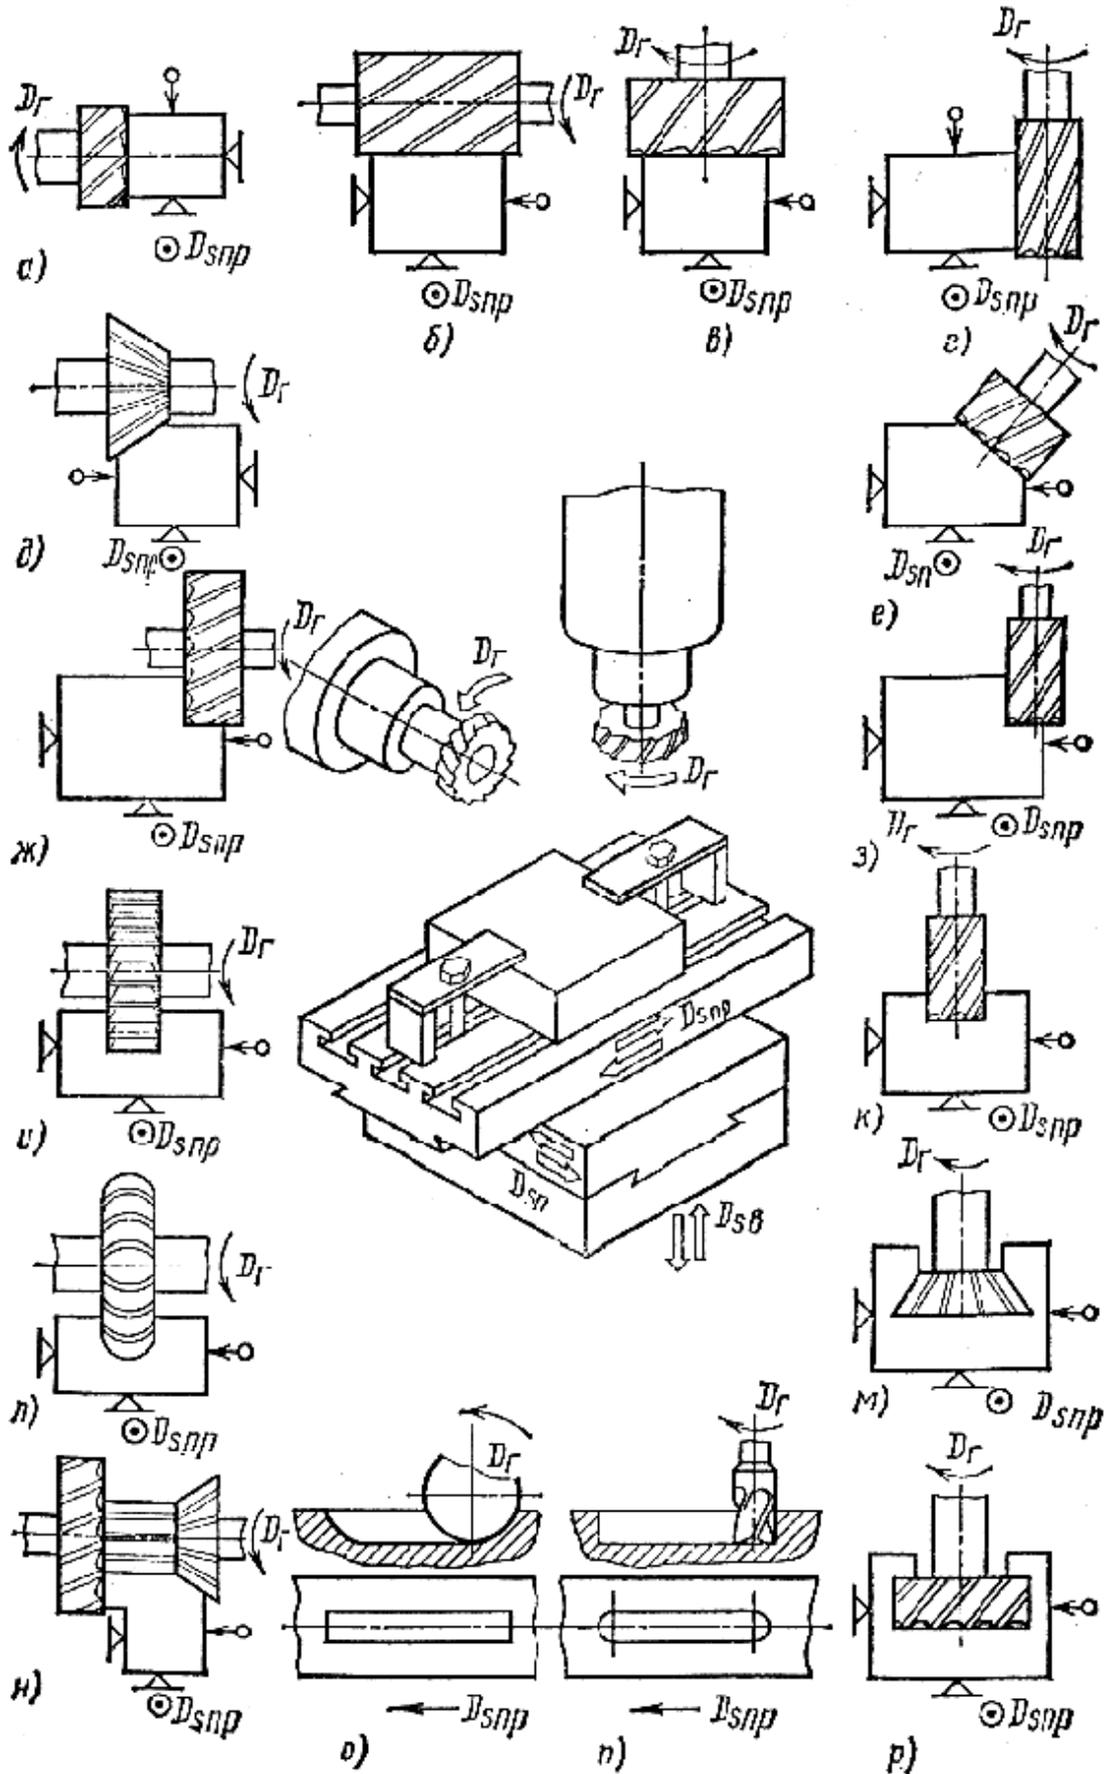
Схемы обработки заготовок на фрезерных станках
